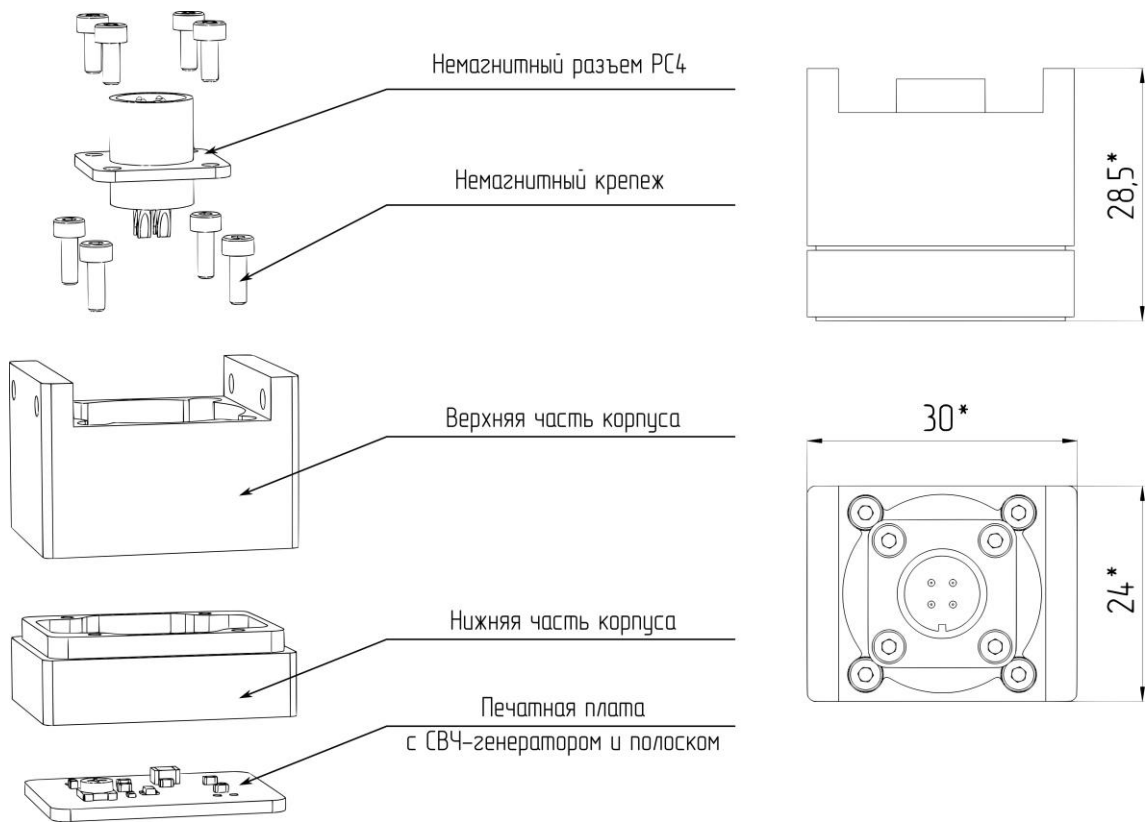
Чертеж с разнесенными частями и габаритный чертеж СВЧ-головки спектрометра ФМР
